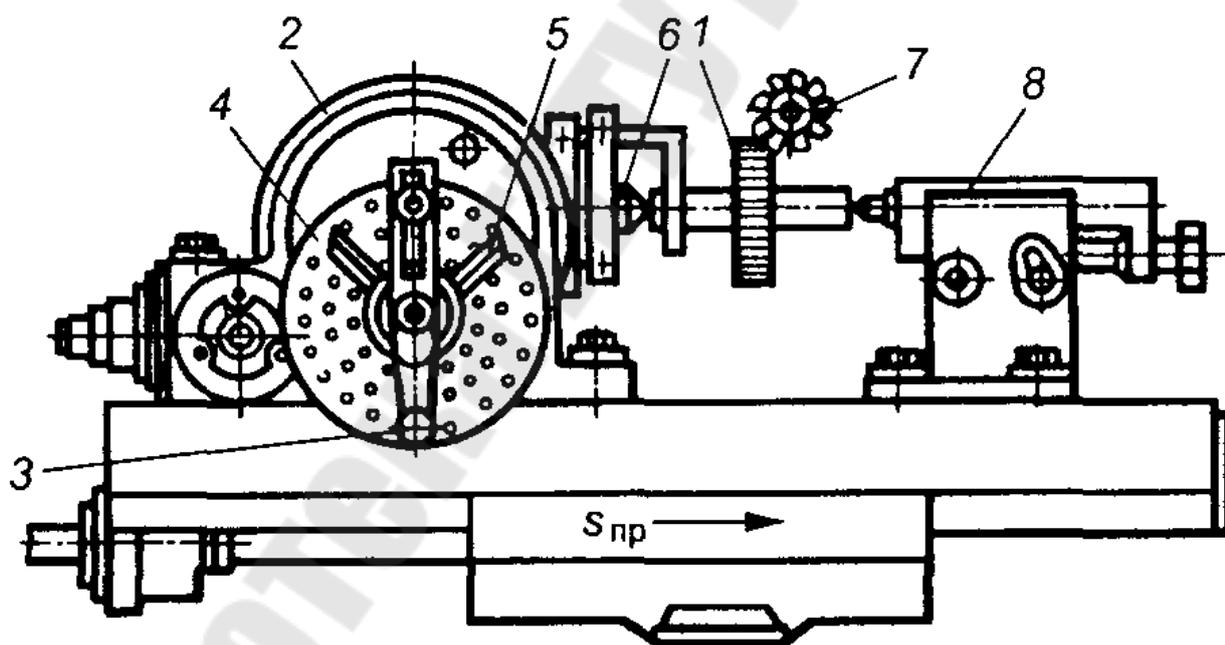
Общий вид универсальной делительной головки и схема установки заготовки
